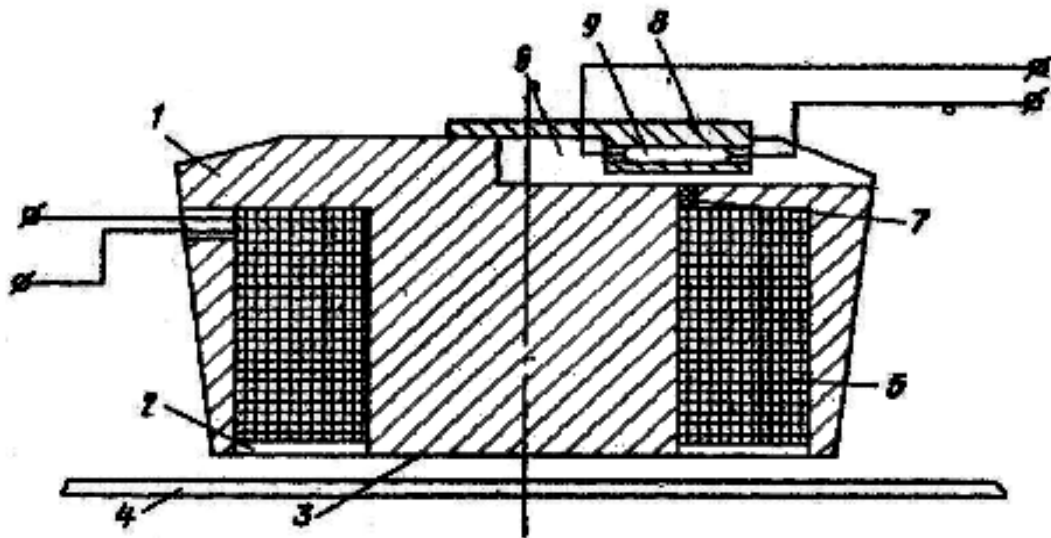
Електромагнітний захват, загальний вигляд
